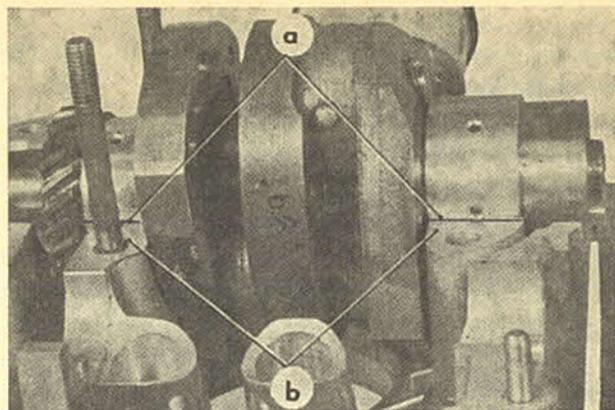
Nut a und Dichtfläche b höhengleich kennzeichnen
